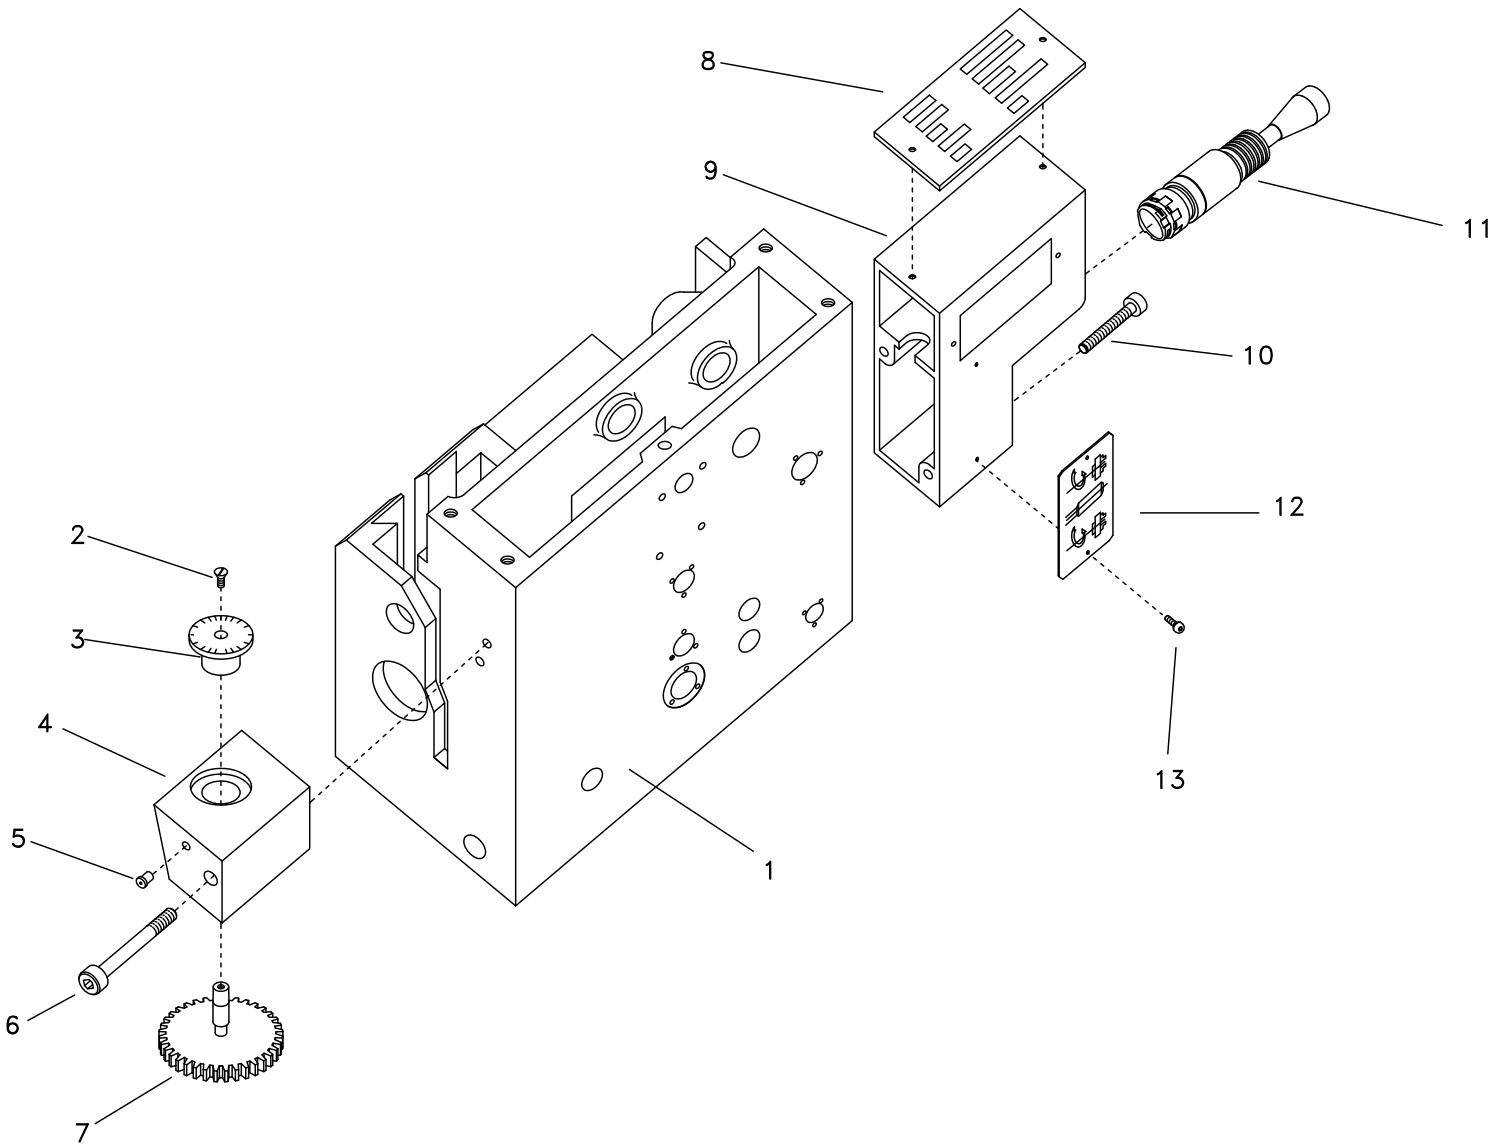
Rozpadové schéma - Suportová skřín 1 ze 2
